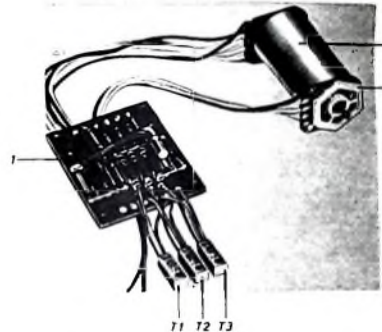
Platine 1 der elektronischen Steuerung des Motors 2, an dessen vorderem Flansch die Aufhängung 3 für die Montage erkennbar ist
